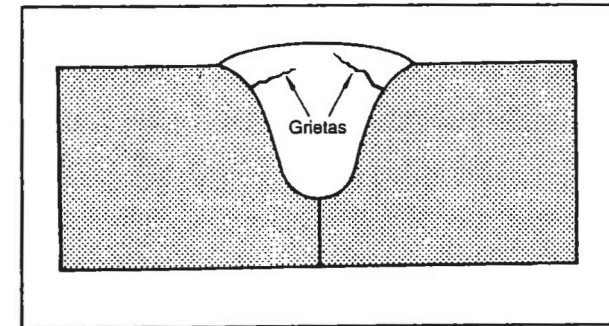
FORMACIÓN DE GRIETAS EN EL CORDÓN DE SOLDADURA DEBIDO A LA BAJA VELOCIDAD DE SOLDEO y LA ALTA TENSIÓN
